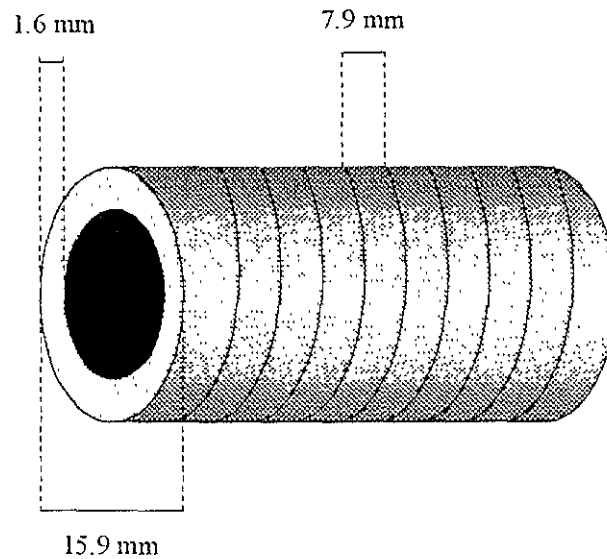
Dimensiones del tubo corrugado utilizado en el TAS.
